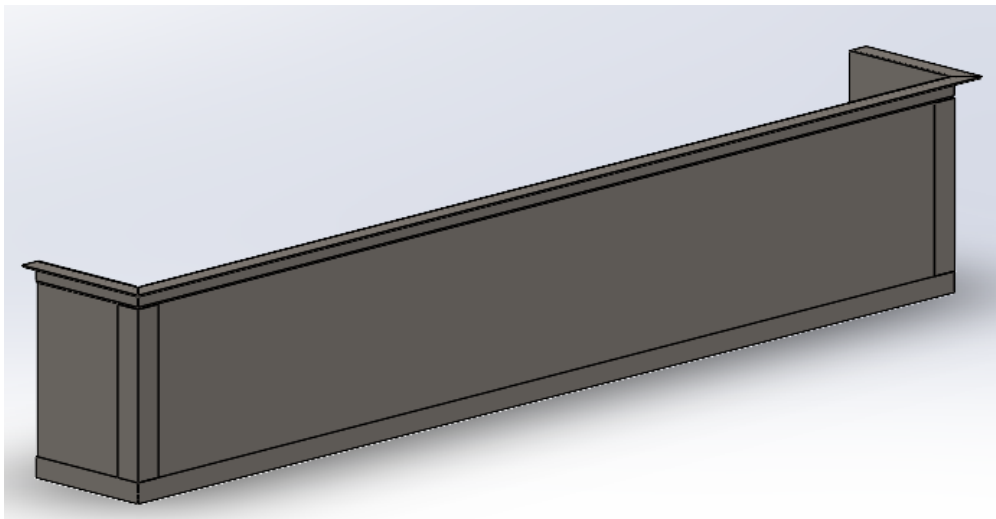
Vista parcial de los refuerzos en la estructura.
